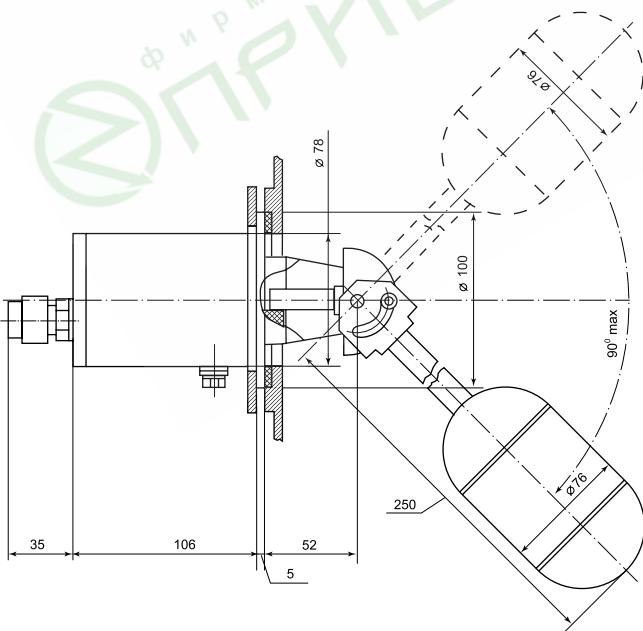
Габаритные и присоединительные размеры РОС 400-8
